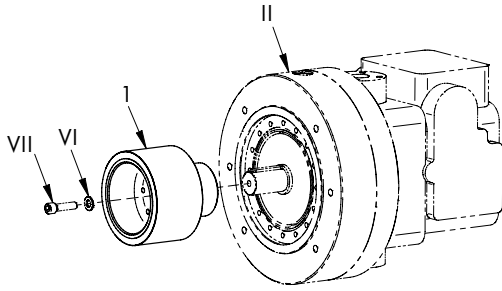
Montage des Innenrotors an die Abtriebsseite (A1)
